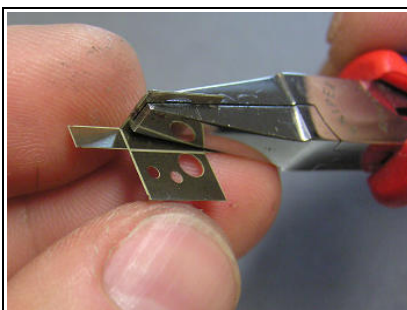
Die geätzten Nuten (Biegekante) liegen innen. Erstes Seitenblech um 90° aufbiegen.
